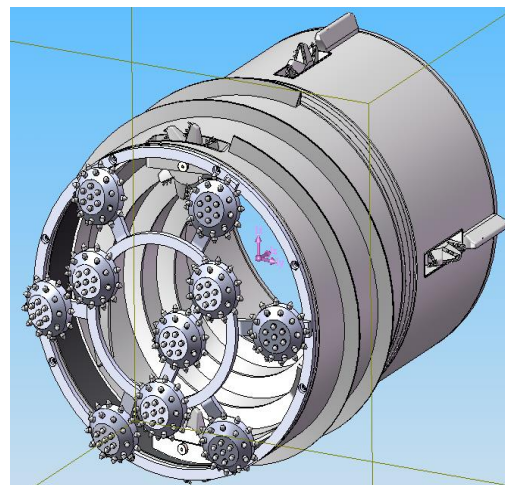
Проходческий агрегат геоход [Tunnel boring machine - geokhod]
